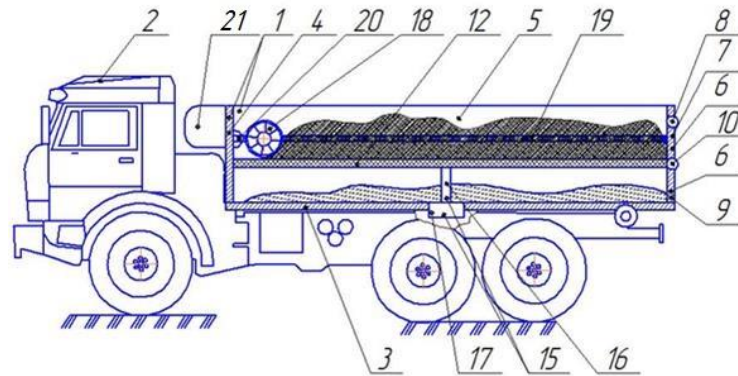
Схема конструкції молотильного пристрою люцерни на базі автомобіля: 1 – кузов; 2 – транспортний засіб; 3 – дно кузова; 4 – передній борт; 5 – бічні борти; 6 – задній борт; 7 – верхня частина заднього борту; 8 – шарнір; 9 – нижня частина; 10 – шарнір; 11 – гідроциліндр; 12 – перфорована гнучка мембрана (дека-решето); 13 – акумулятор; 14 – сітка; 15 – вібропривід; 16 – кінематичний зв'язок вібратора та деки-решета; 17 – вібратор; 18 – обмолочувальний барабан; 19 – напрямні; 20 – лебідка, 21 – акумуляторна батарея.
